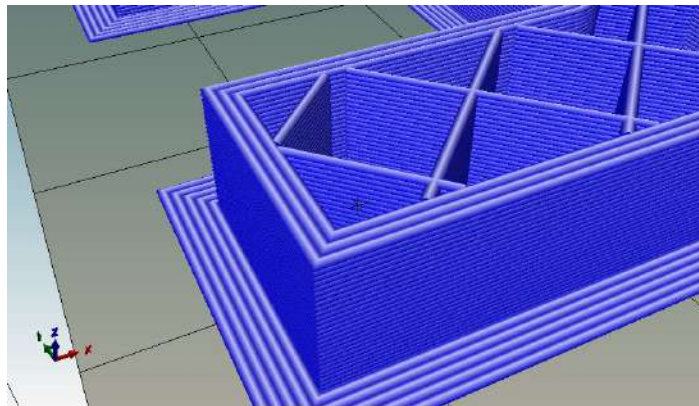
Preenchimento interno e externo de peças - Repetier Host
